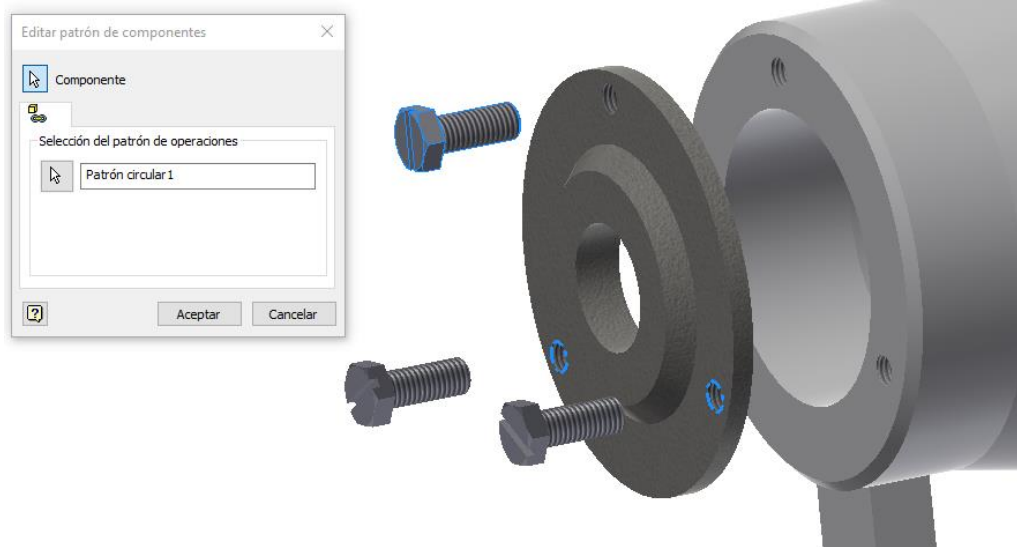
Inserción de tornillos en el montaje de la tapa de rodamientos
